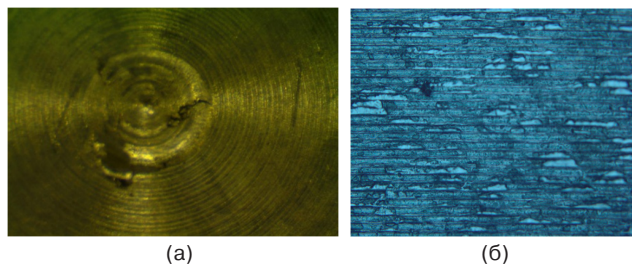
Поверхность исходной заготовки с вырывом материала в процессе токарно-механической обработки и стружкой на ее поверхности (а); полученная послековки поверхность с прослойками включений (б)
